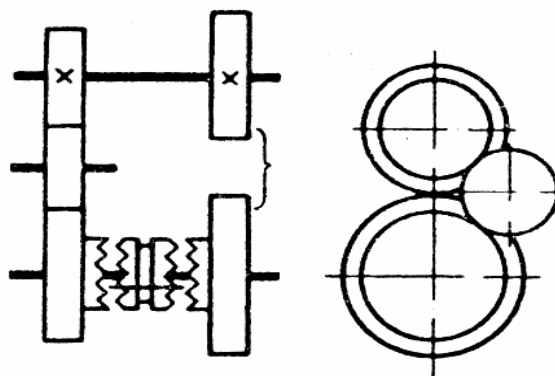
Реверсивный механизм с цилиндрическими колесами
